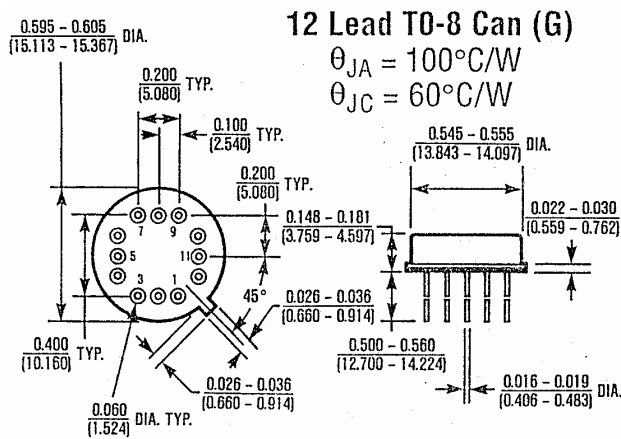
Esquema Técnico de la Cápsula *TO-8* utilizada.
